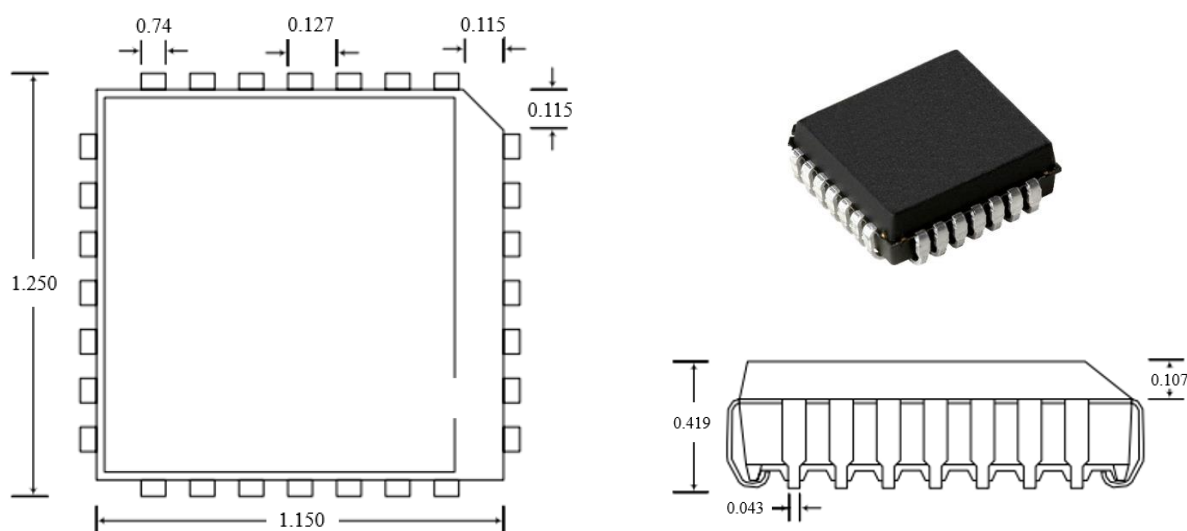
Пластиковый LCC корпус с 28 контактами
